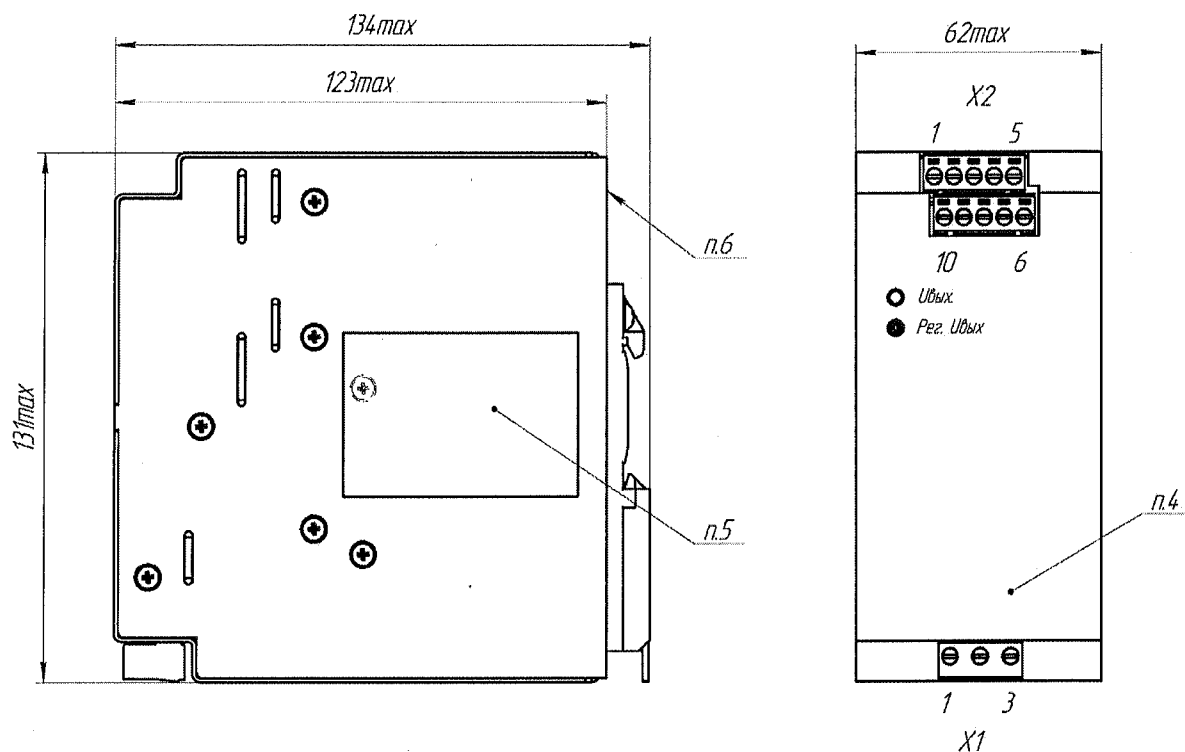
Габаритные размеры модуля КАН-Д480
